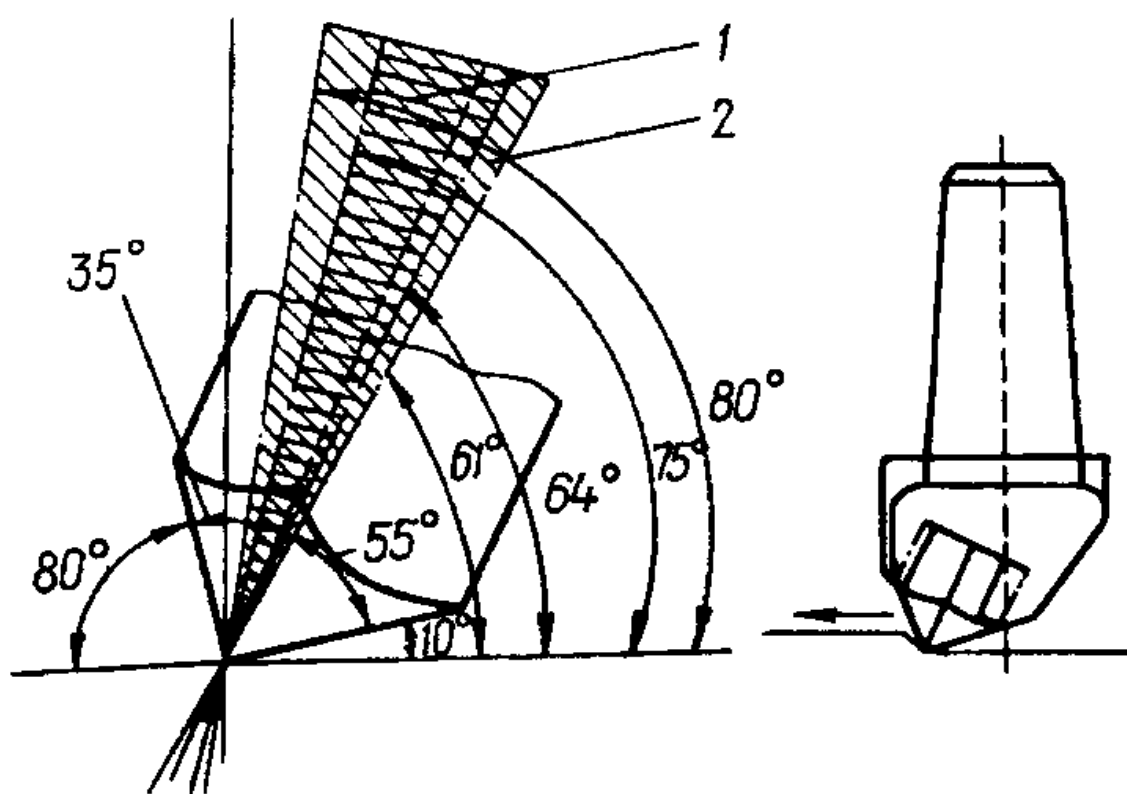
Схема раціонального розташування ріжучої вставки в корпусі різця:
